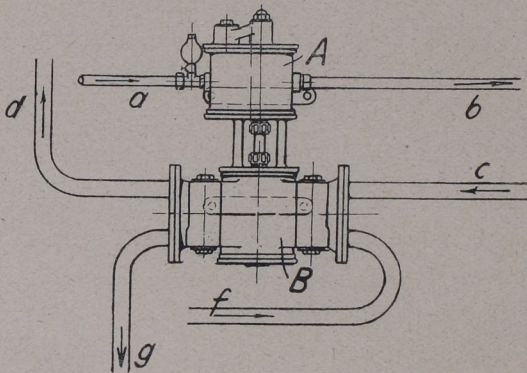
Speisewasserpumpe Bauart „Caille“.
